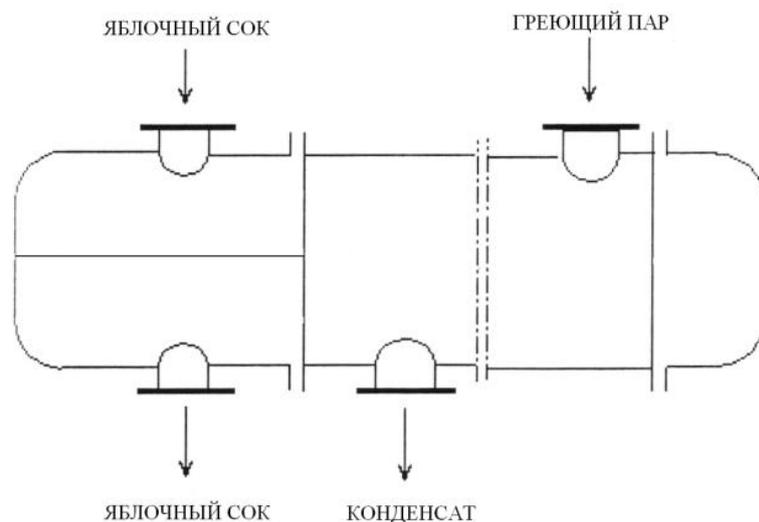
Двухходовой кожухотрубчатый теплообменник
